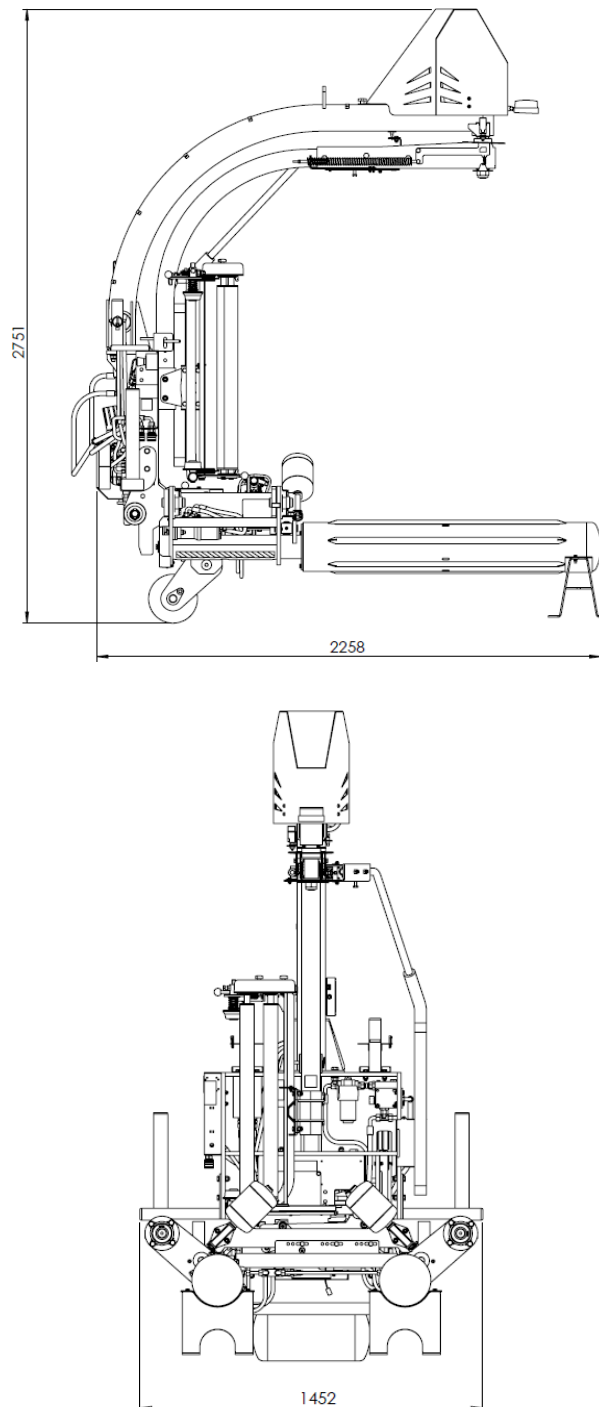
Габаритные размеры обмотчика в транспортном положении
